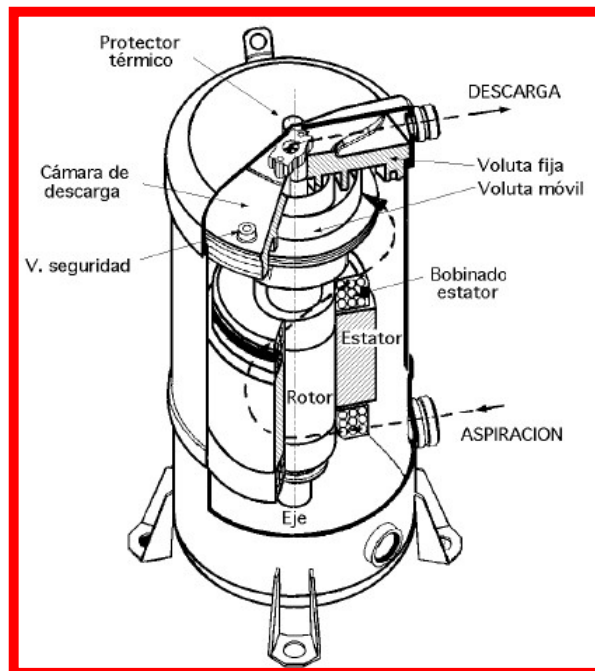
Vista del conjunto árbol-rotor del compresor scroll.+
